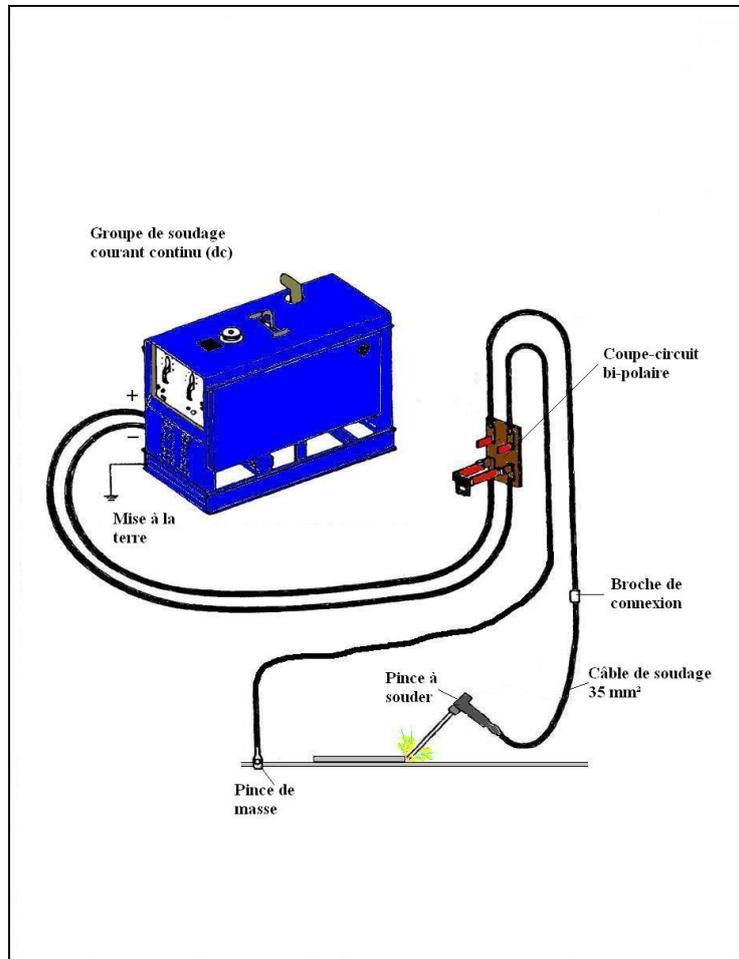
Installation pour le soudage en pleine eau
